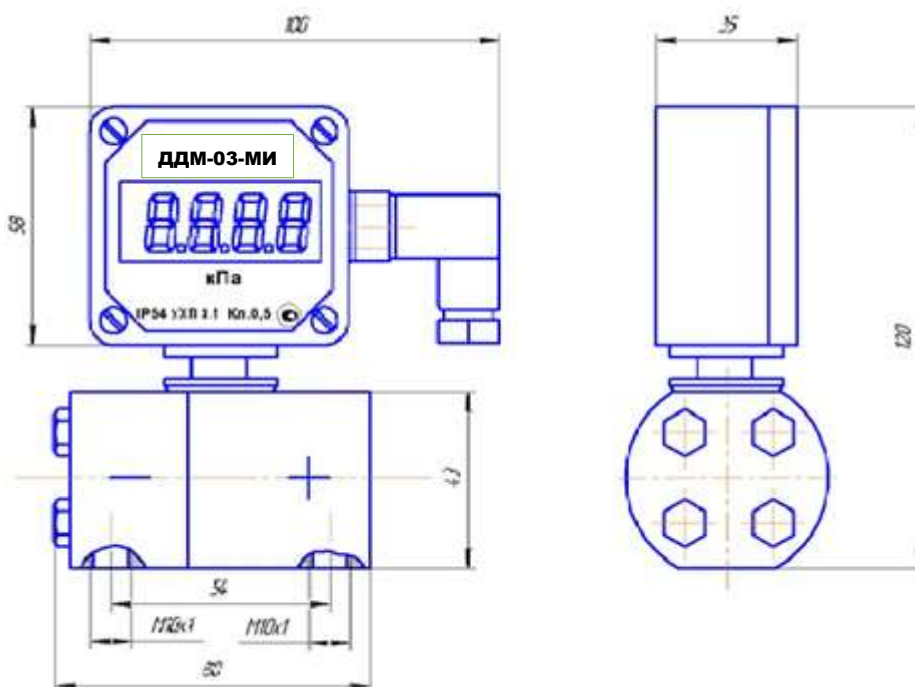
Габаритные и присоединительные размеры датчика ДДМ-03-ДД-МИ-03
